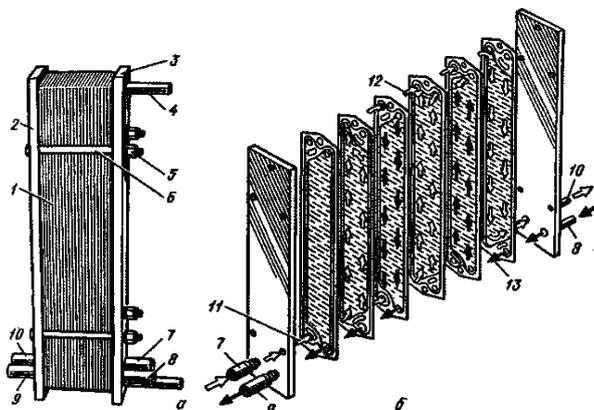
Устройство охладителя ОМ-400 (а) и схема движения в нем молока и воды (б): 1 - комплект теплообменных пластин; 2 - упорная плита; 3 - нажимная плита; 4 - штанга; 5 - гайка; 6 - шпилька; 7, 10 - патрубки соответственно для подво-
